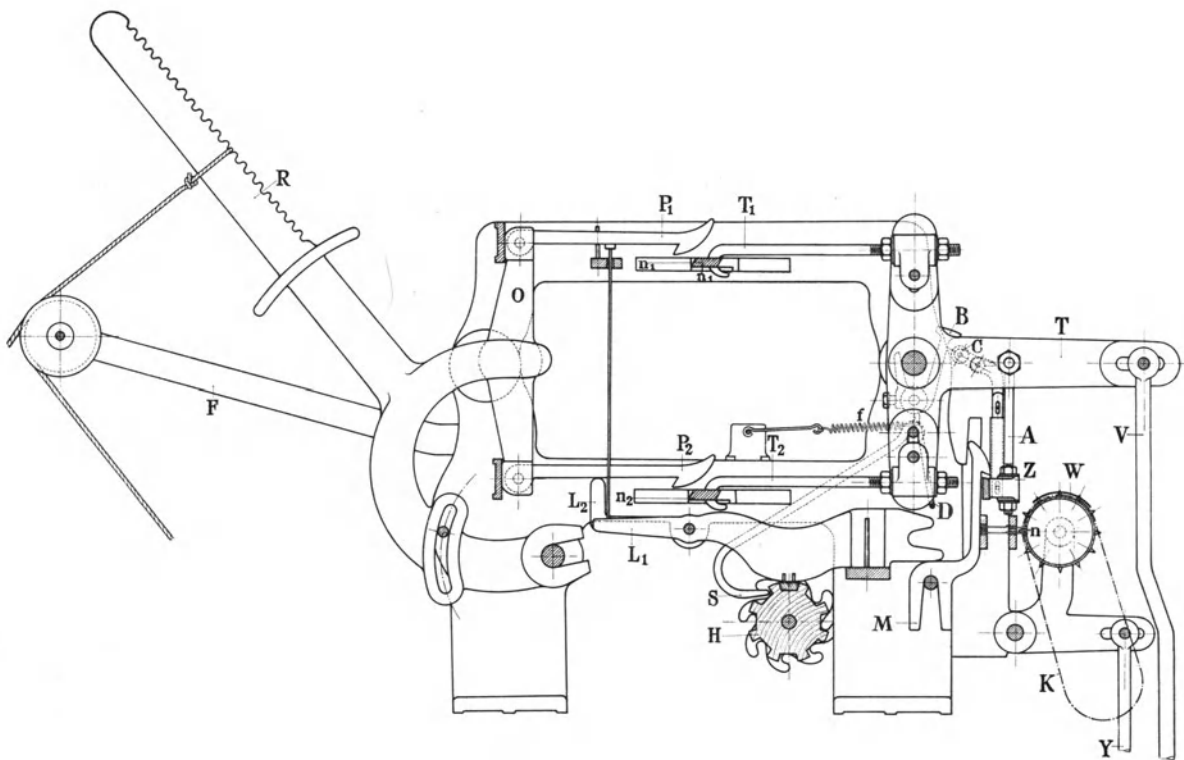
Die Schaftmaschine von Stäubli mit Holzkarten und endloser Papierkarte.
